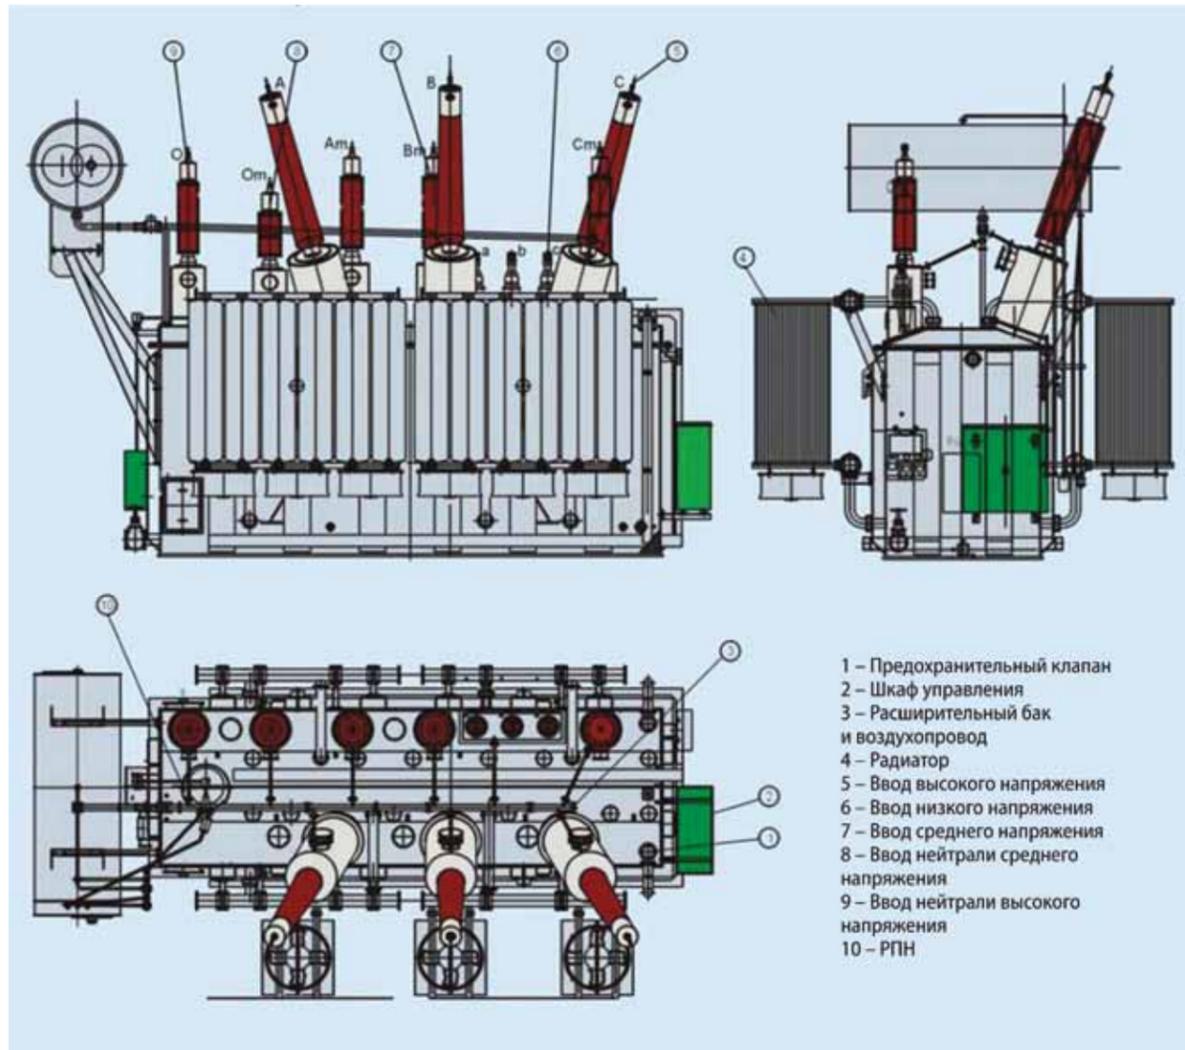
Внешний вид и размеры трехфазного трансформатора с регулированием напряжения под нагрузкой 220 кВ
